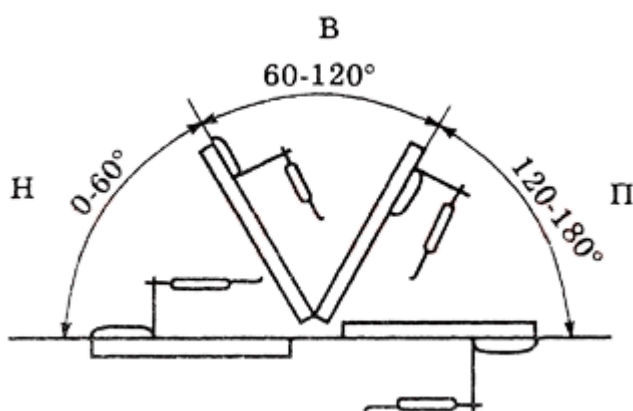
Различные положения изделия при ручной дуговой сварке
